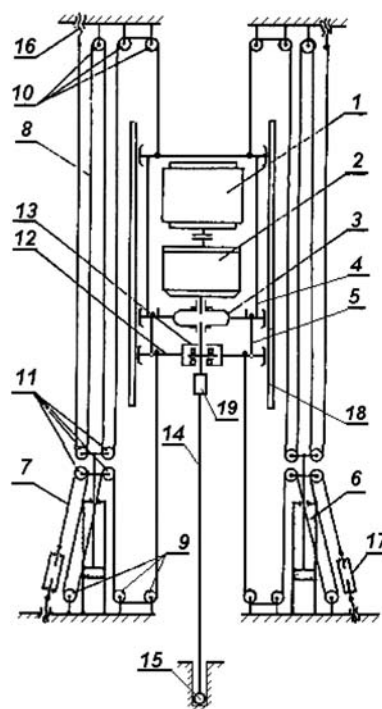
Схема вращательно-подающего механизма станка СБШ-250: 1 — электродвигатель; 2 — редуктор; 3 — шинно-зубчатая муфта; 4 — каретка привода вращателя; 5 — тяга "каретка-напорная траверса"; 6 — гидродомкраты подачи; 7 — напорный канат; 8 — подъемный канат; 9 — неподвижные блоки в нижнем основании мачты; 10 — неподвижные блоки в верхней части мачты; 11 — подвижные блоки; 12 — напорная траверса; 13 — опорный узел; 14 — буровой став; 15 — долото; 16 — регулировочные болты; 17 — регулировочные муфты; 18 — направляющие швеллеры опорного узла и каретки привода вращателя; 19 — муфта шпинделя вращателя
